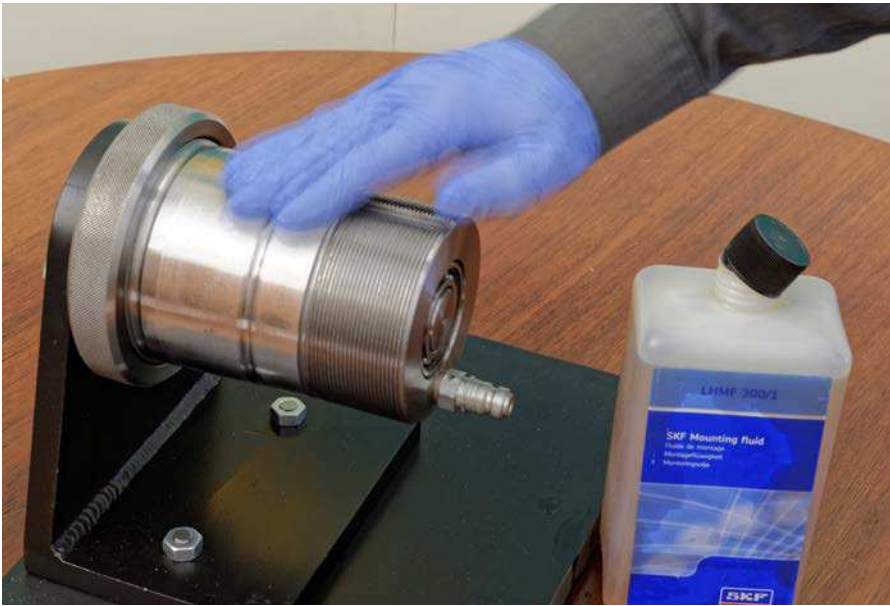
Lubrique con aceite el asiento del rodamiento y la rosca de la tuerca hidráulica
